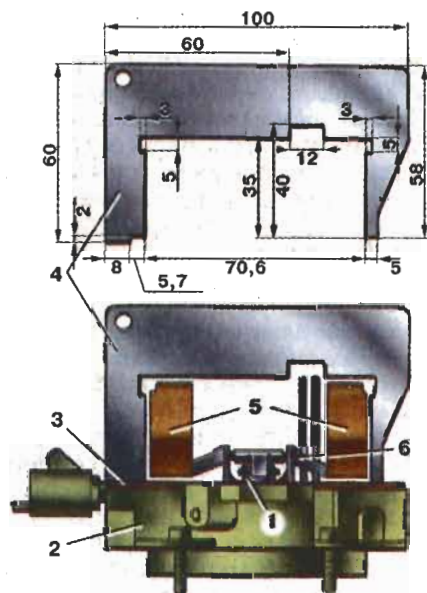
Регулировка положения поплавков с помощью шаблона: 1 – топливный клапан; 2 – крышка карбюратора; 3 – прокладка крышки; 4 – шаблон; 5 – поплавки; 6 – кронштейн поплавков
